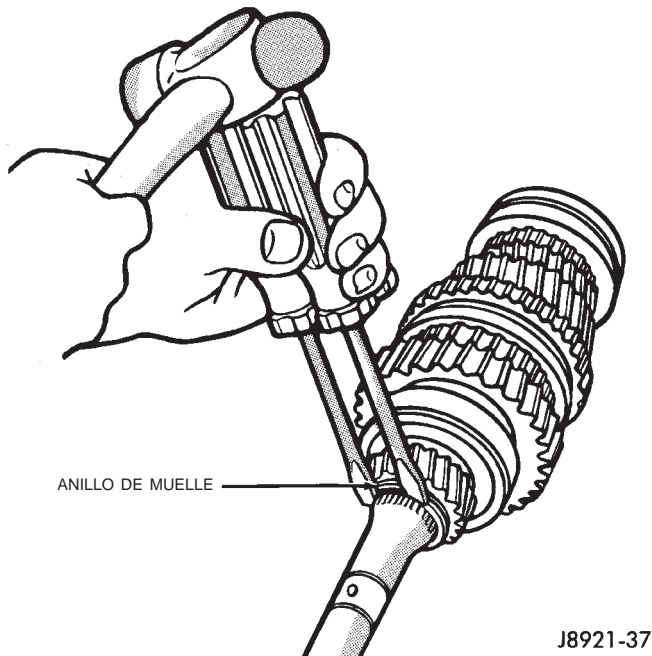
Desmontaje de anillo de muelle de engranaje de quinta velocidad
